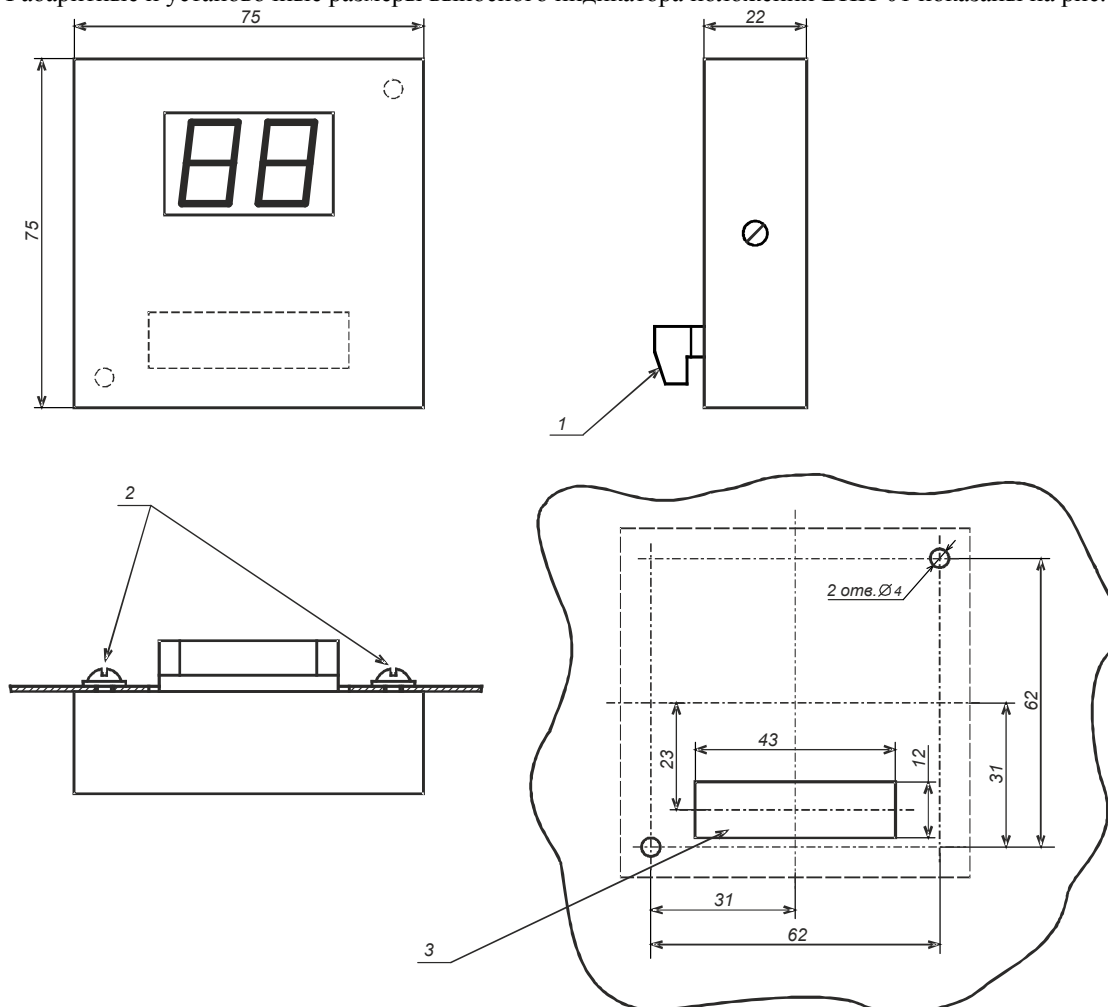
Общий вид и установочные размеры выносного индикатора положений ВИП-01
